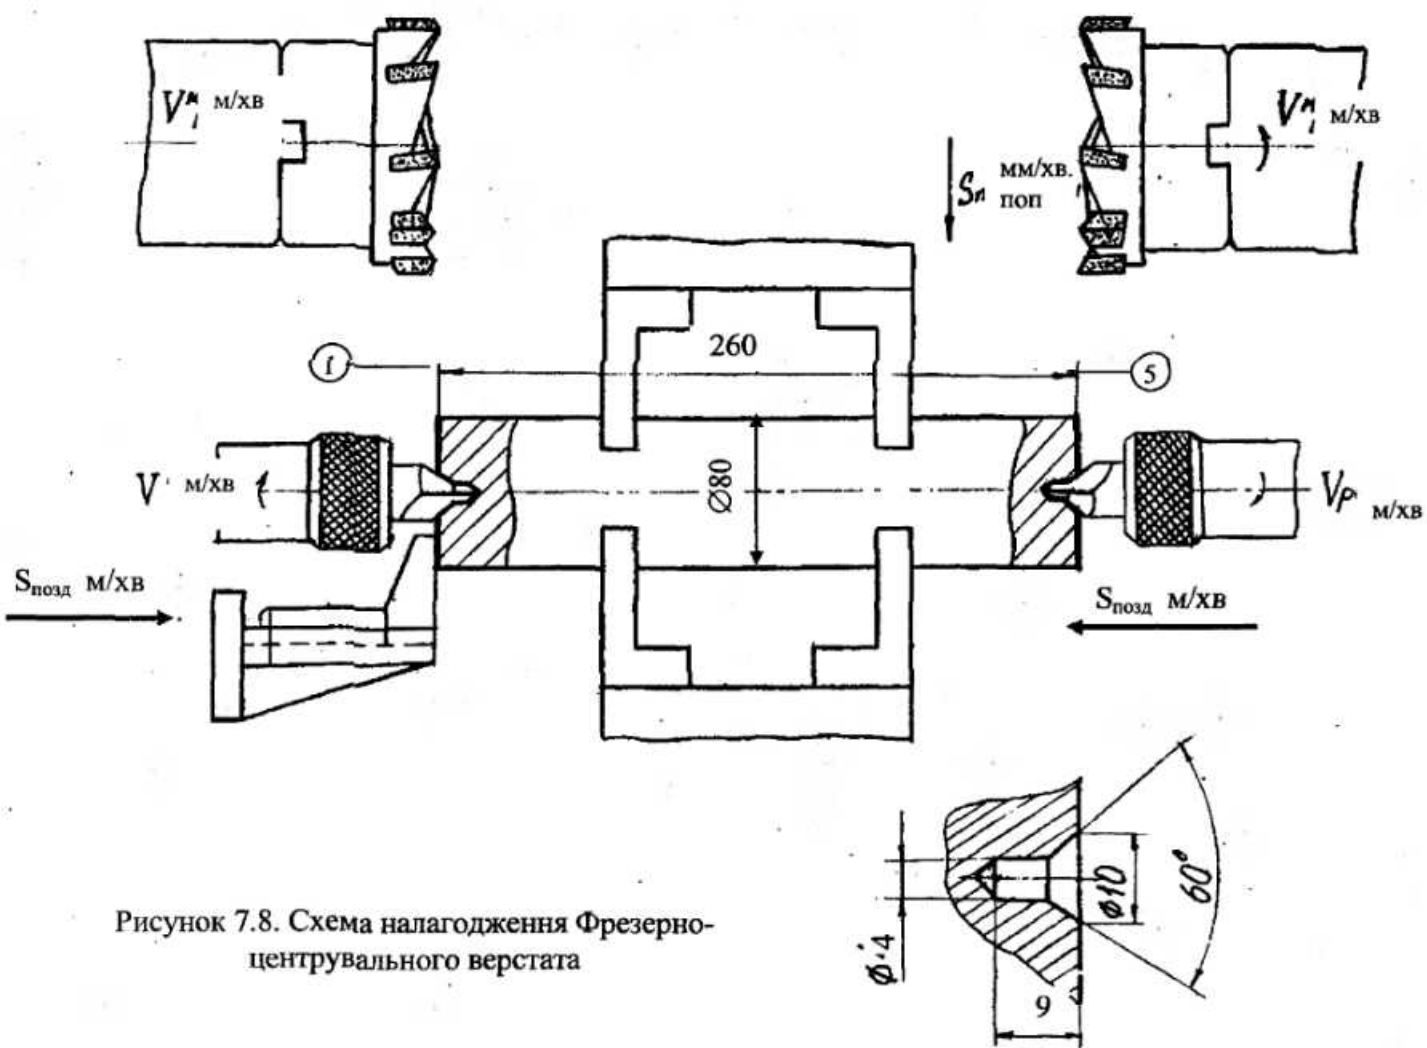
Схема налагодження Фрезерно-центрального верстата
